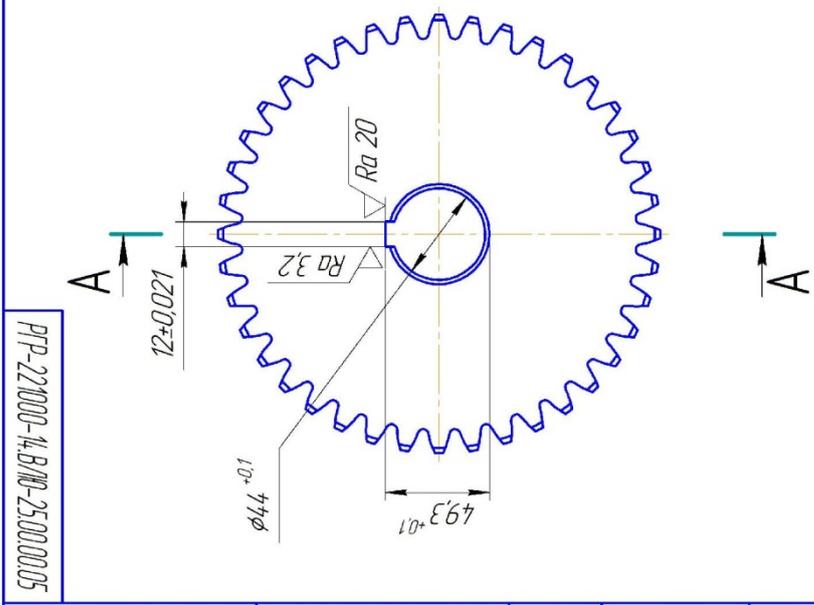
Схема расположения шпоночного паза на зубчатом колесе
